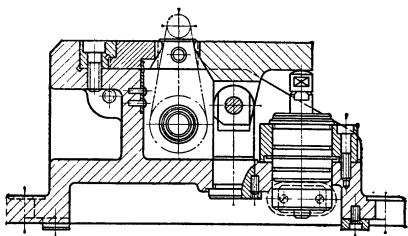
Рычажное приспособление для фрезерования паза в вылке
